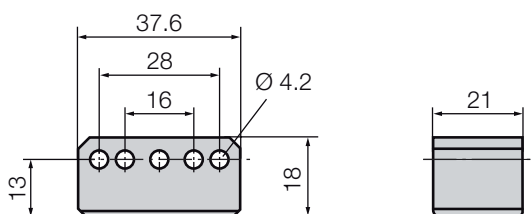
Medidas para montagem do encoder de posição BTL6-A-3801-2
